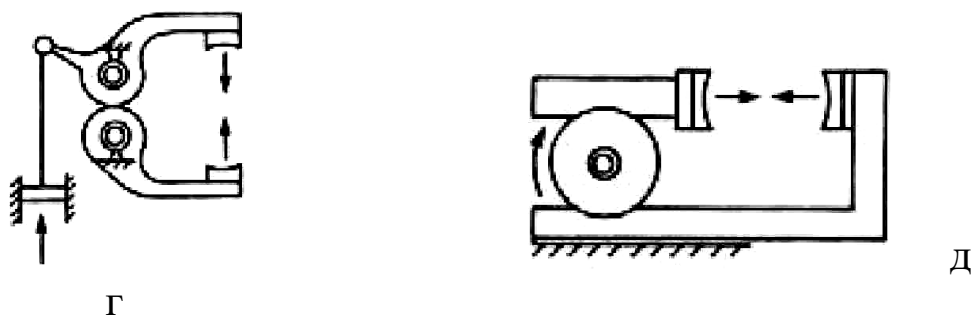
Кінематичні схеми ЗП із зубчато-рейковими проміжними механізмами
